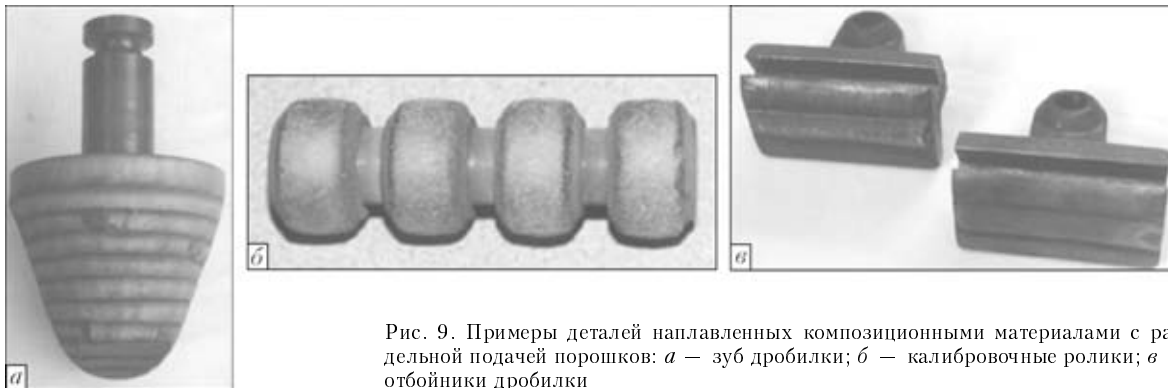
Примеры деталей наплавленных композиционными материалами с раздельной подачей порошков: а — зуб дробилки; б — калибровочные ролики; в — отбойники дробилки
